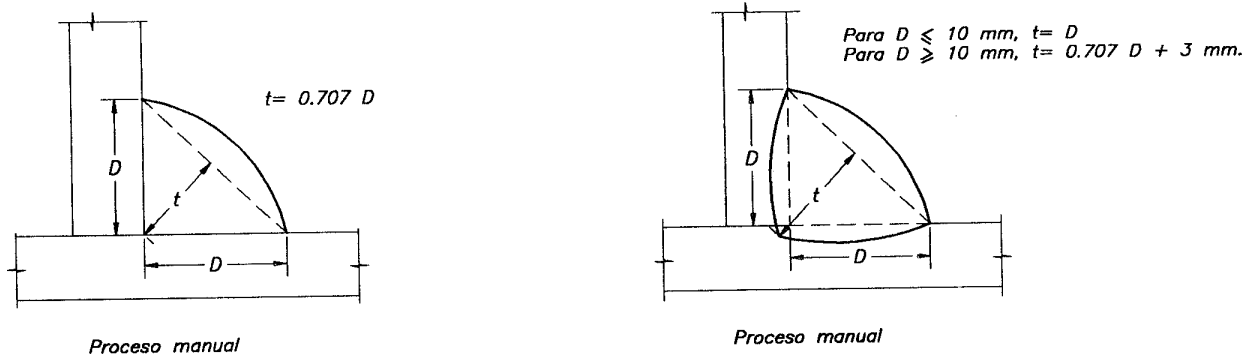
ÁREA EFECTIVA EN UNA SOLDADURA DE FILETE
